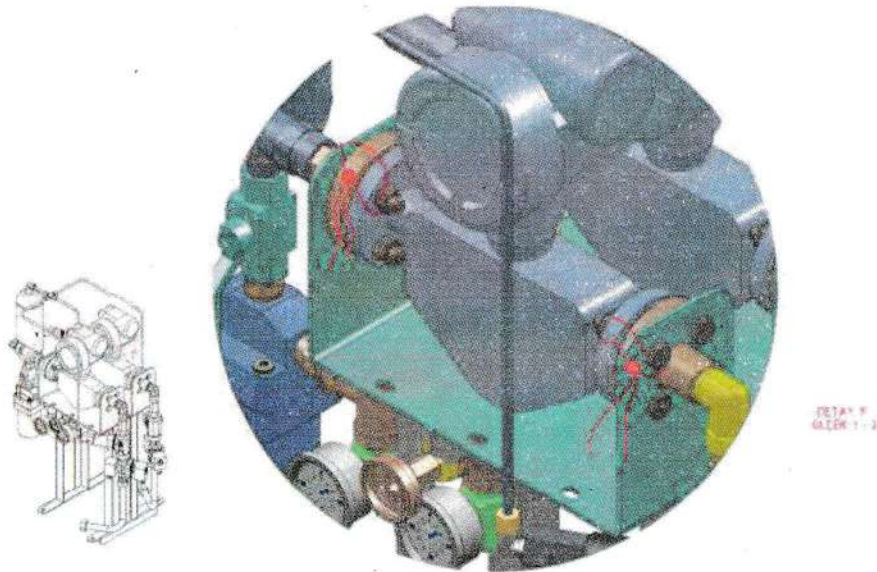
Akış Ölçer (Debimetre) ve Pulser Mühürleme Planı
